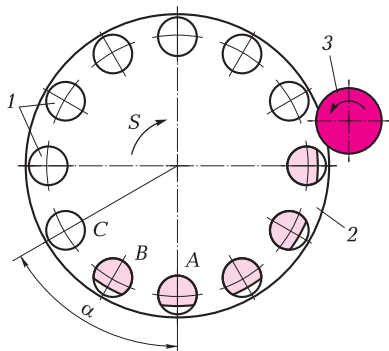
Схема одновременной непрерывной обработки заготовки:
